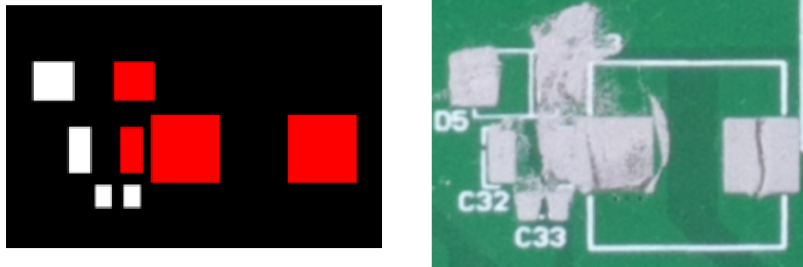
Detalhe da inspeção *pad a pad*, resultado da inspeção à esquerda e imagem capturada à direita.
